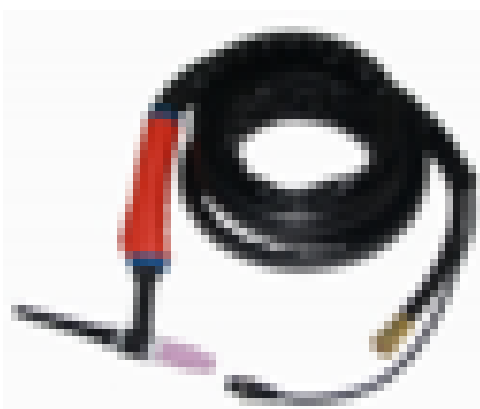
Общий вид горелки WP-26F 180A
